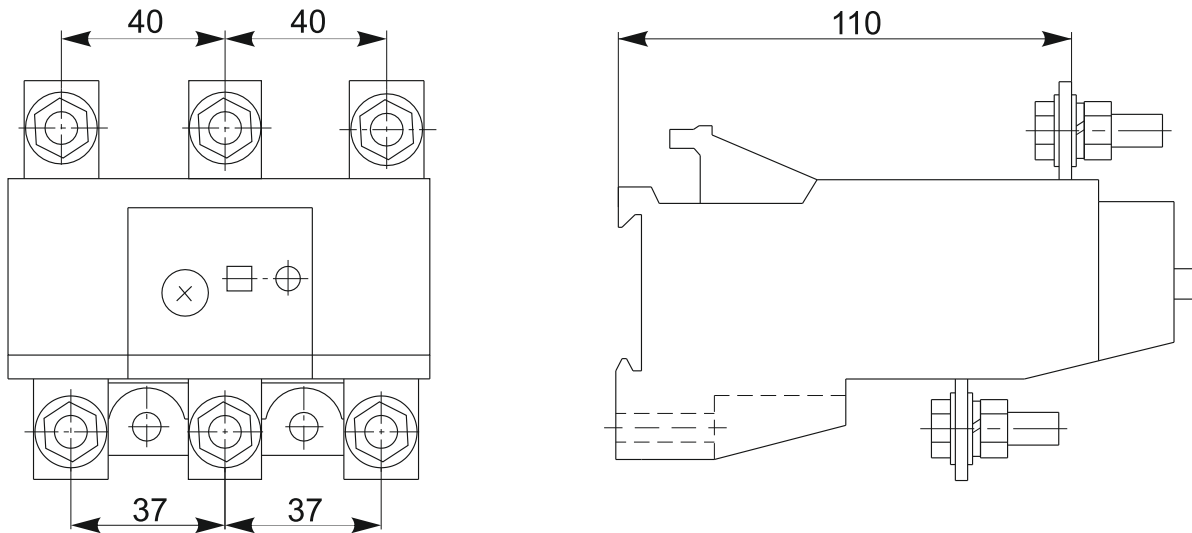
Габаритні, установочні та приєднувальні розміри РТ-4055080, РТ-4063090, РТ-4080110, РТ-4090120, РТ-4110135, РТ-4120150, РТ-4135160, РТ-4150180, варіант 2
